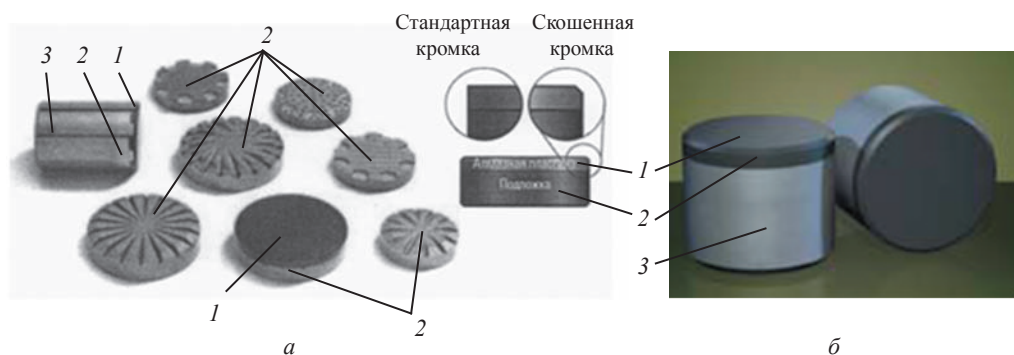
Возможные формы пластинок (а) и резцов PDC (б): 1 – поликристаллические алмазы; 2 – подложка из твердого сплава; 3 – корпус резца
